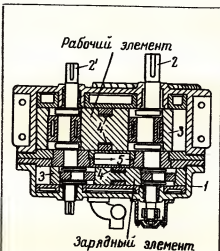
Конструкция основных элементов ротативно-поршневого двигателя «Рогус».
